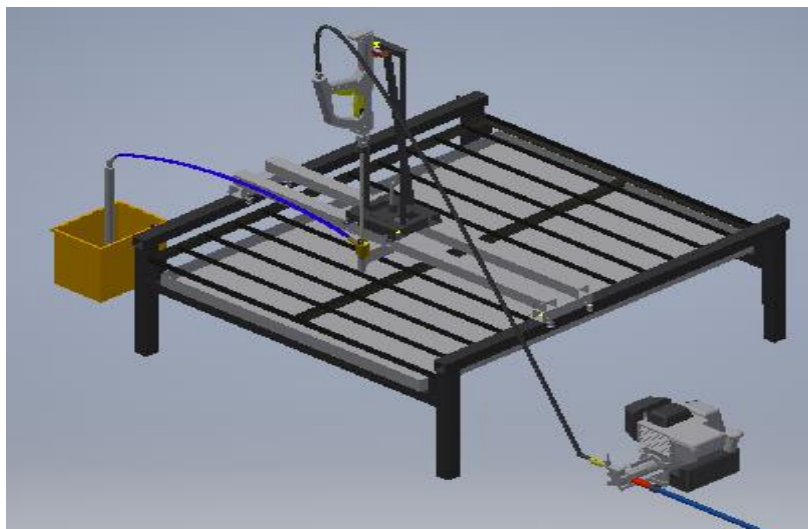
Prototipo de máquina de corte por chorro de agua abrasivo ensamblado en INVENTOR
